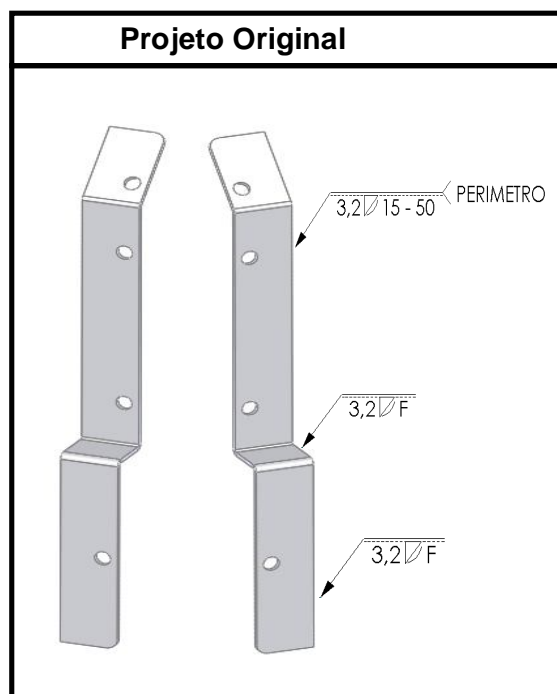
SUPORTE DE FIXAÇÃO : PROJETO ORIGINAL
